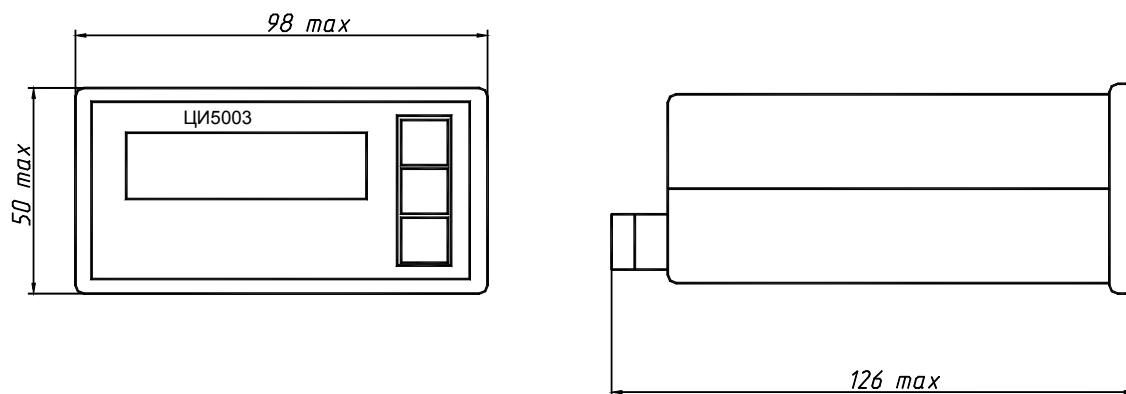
Габаритные размеры прибора ЦИ5003.
